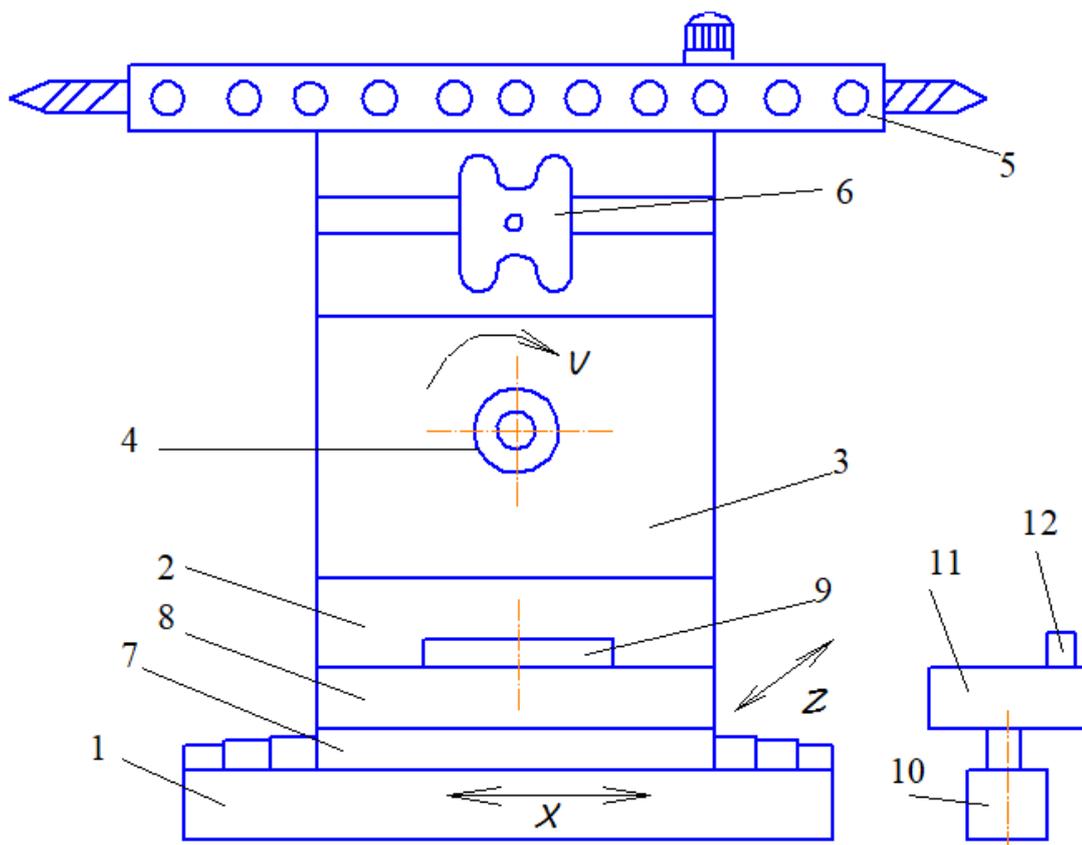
Компоновка многоцелевого станка IP500ПМФ4
